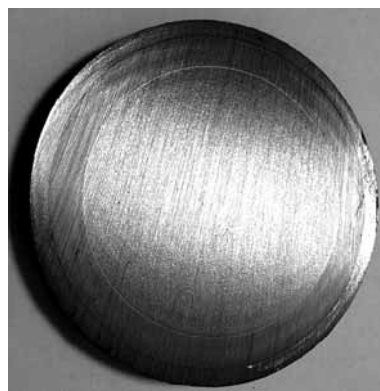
Макротемплет биметаллической заготовки Р6М5/5ХНМ
